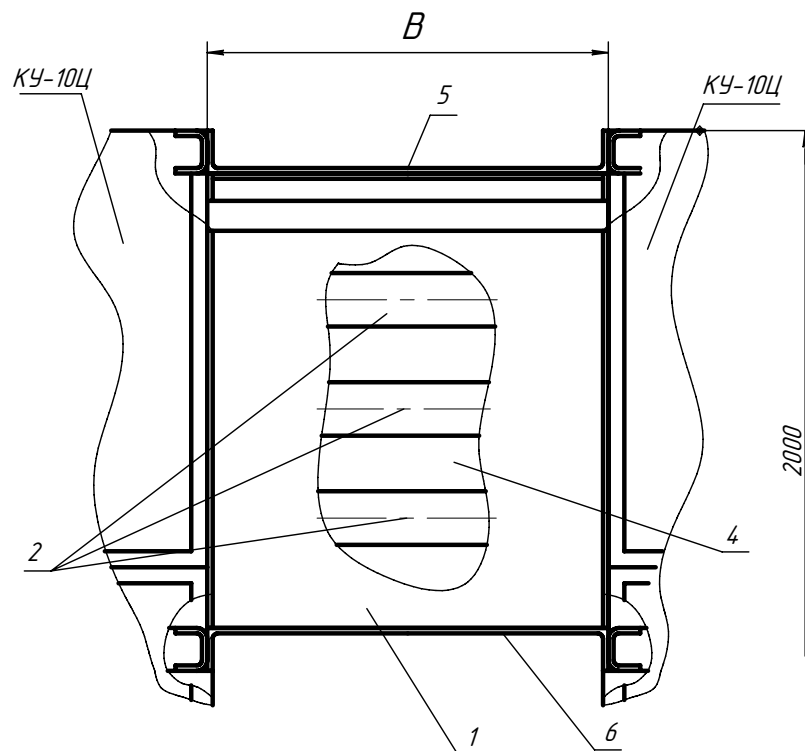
Габаритные, установочные, присоединительные размеры шкафов.
